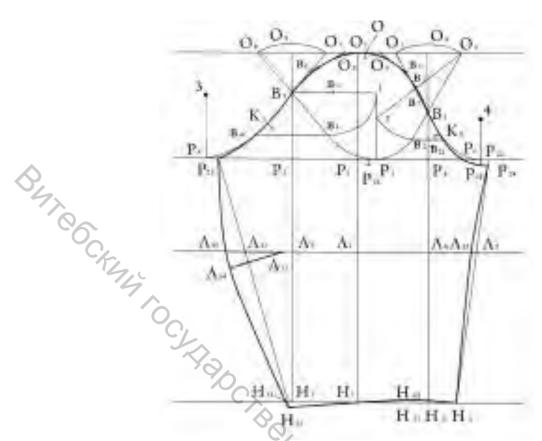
Чертеж базовой конструкции одношовного рукава
